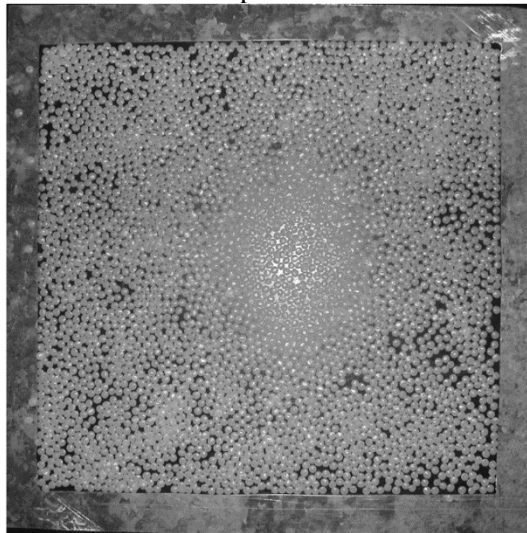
Moldagem por compressão de grânulos, utilizando um molde com cavidade
